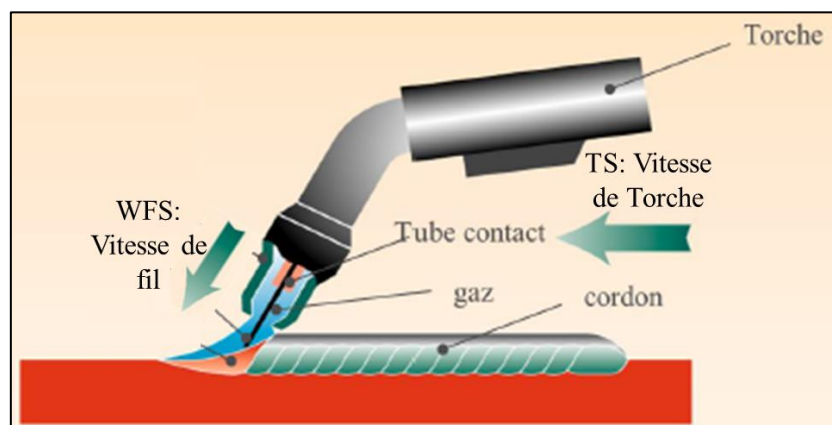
Schéma de principe de soudure MIG (FRONIUS France, 2017b)
